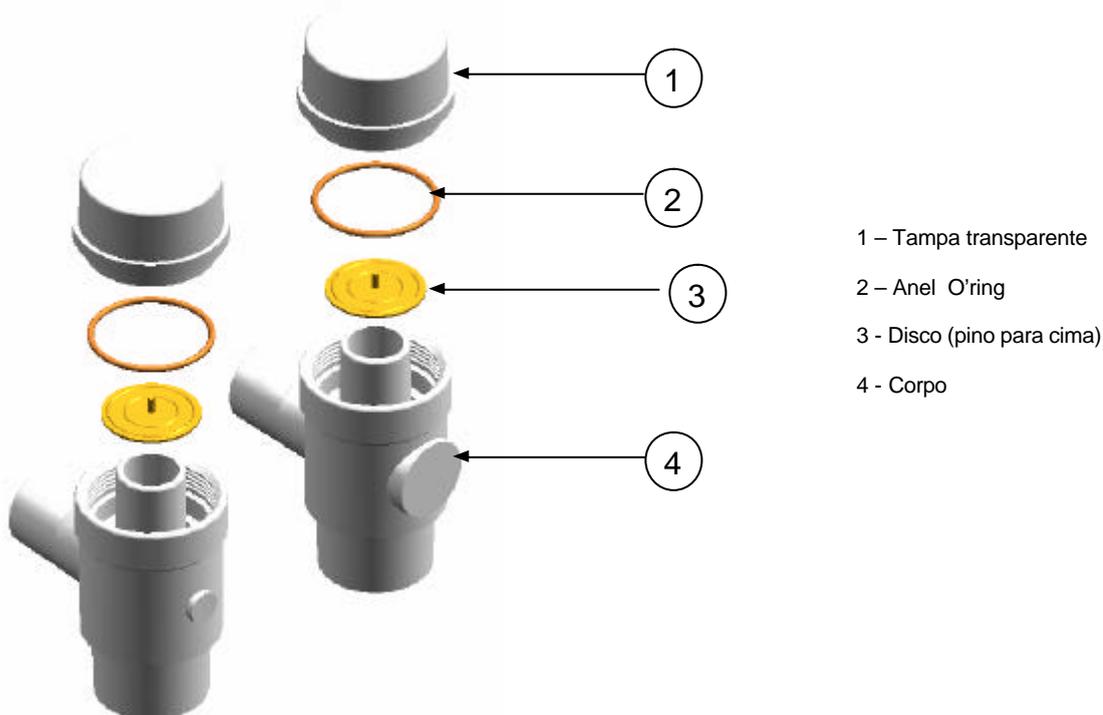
Montagem das válvulas inspiratória e expiratória
